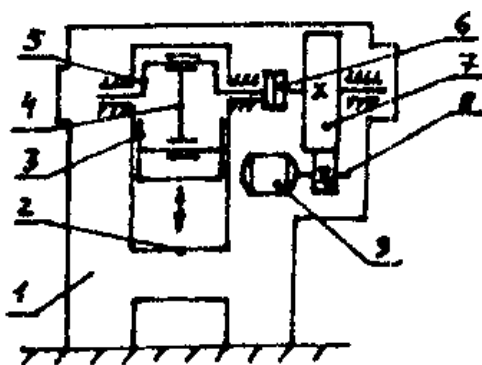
Схема кривошипного пресса: 1 - станина; 2 - стол пресса; 3 - ползун; 4 - шатун; 5 - коленчатый вал; 6 - соединительная муфта; 7 - маховик; 8 - шестерня; 9 - электродвигатель
